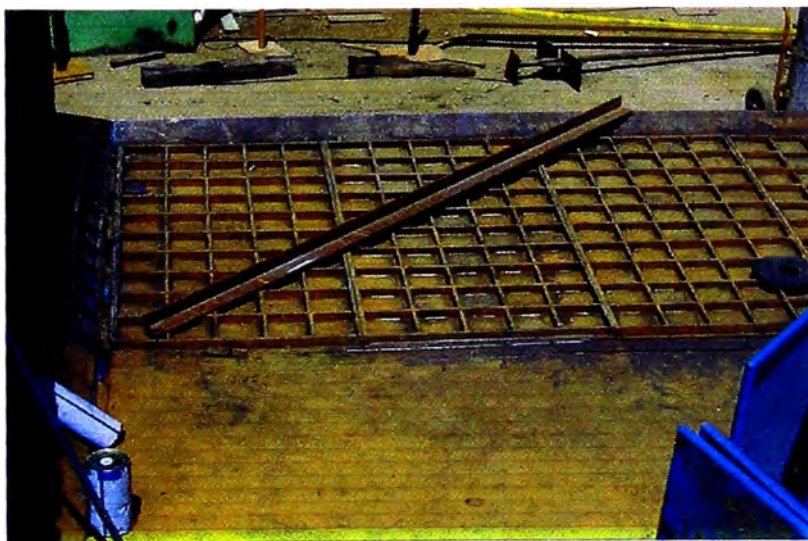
Instalación de planchas antidesgaste y entramado en zona final de cola
